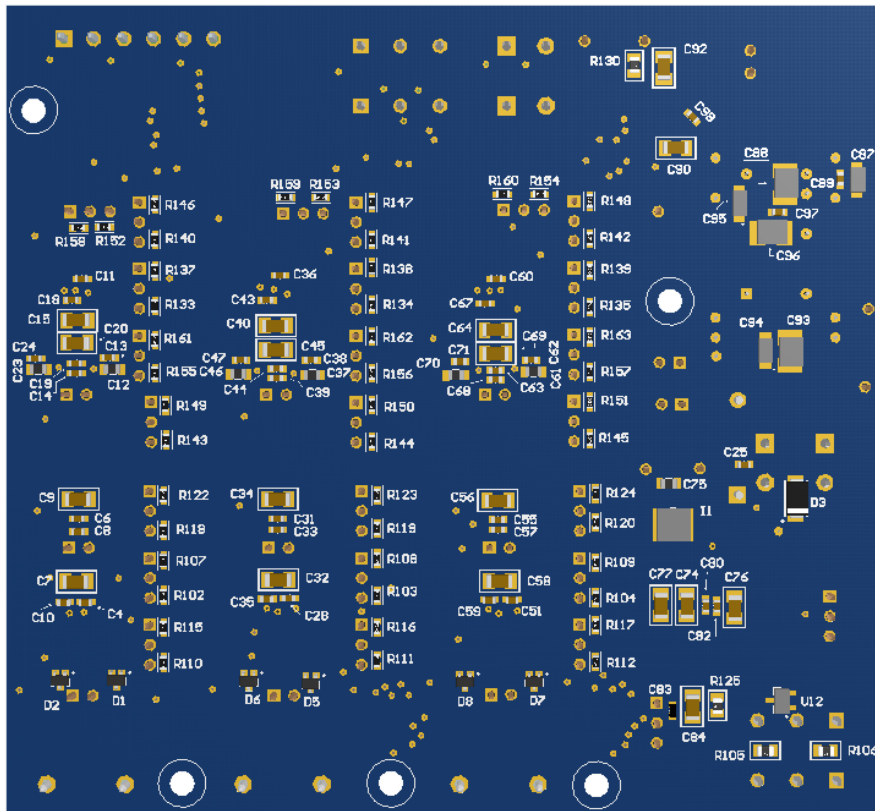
Desenho PCB da placa SMTGI, camada inferior.
